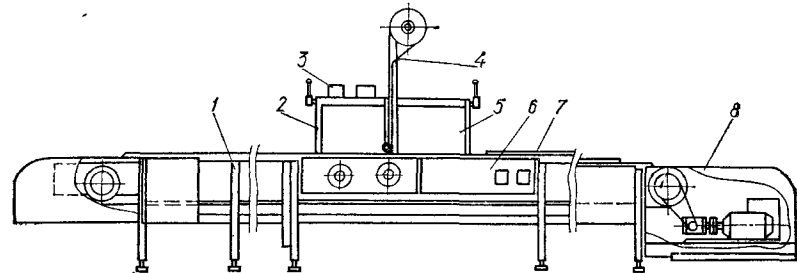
Конвейерная линия непрерывной сварки ковров из линолеума:
